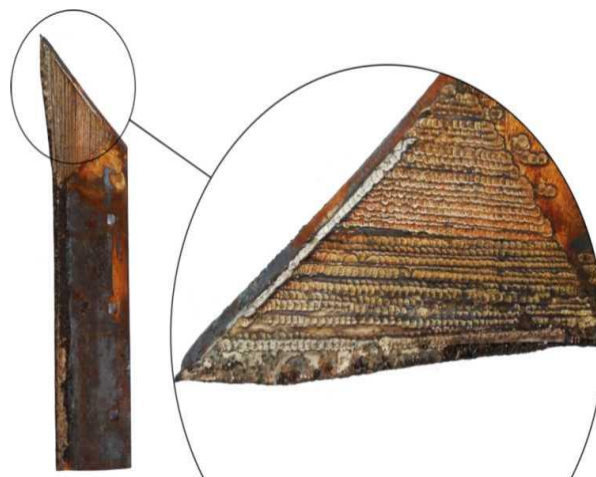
Електроконтактне паяння металевої стрічки до поверхні леміша: а – вид зверху; б – вид з переду
